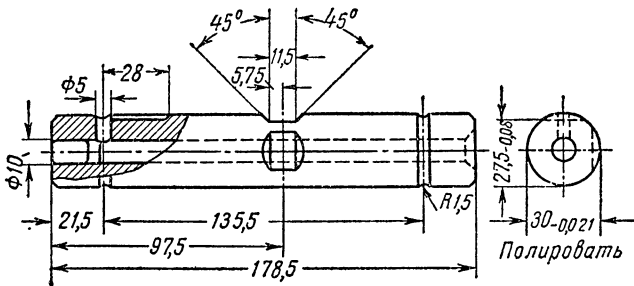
Втулка шкворня поворотного кулака, изготовленная из оловянистого томпка.
